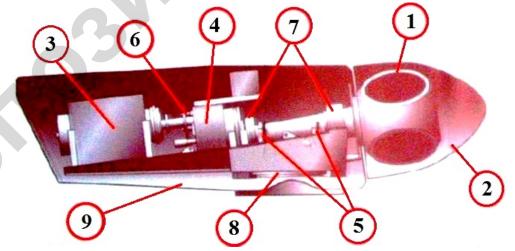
Схема основных элементов (узлов) типовой ВЭУ: I — втулка ветроколеса; 2 — обтекатель; 3 — генератор; 4 — мультипликатор; 5 — следящая система; 6 — дисковый тормоз; 7 — основной вал; 8 — подшипник азимута; 9 — рама гондолы
